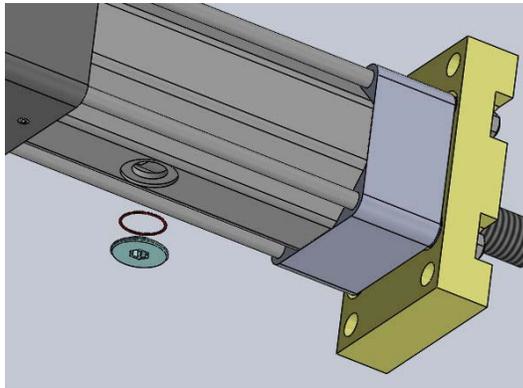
Explosionsansicht RSX-Schmierzugriffsabdeckung
